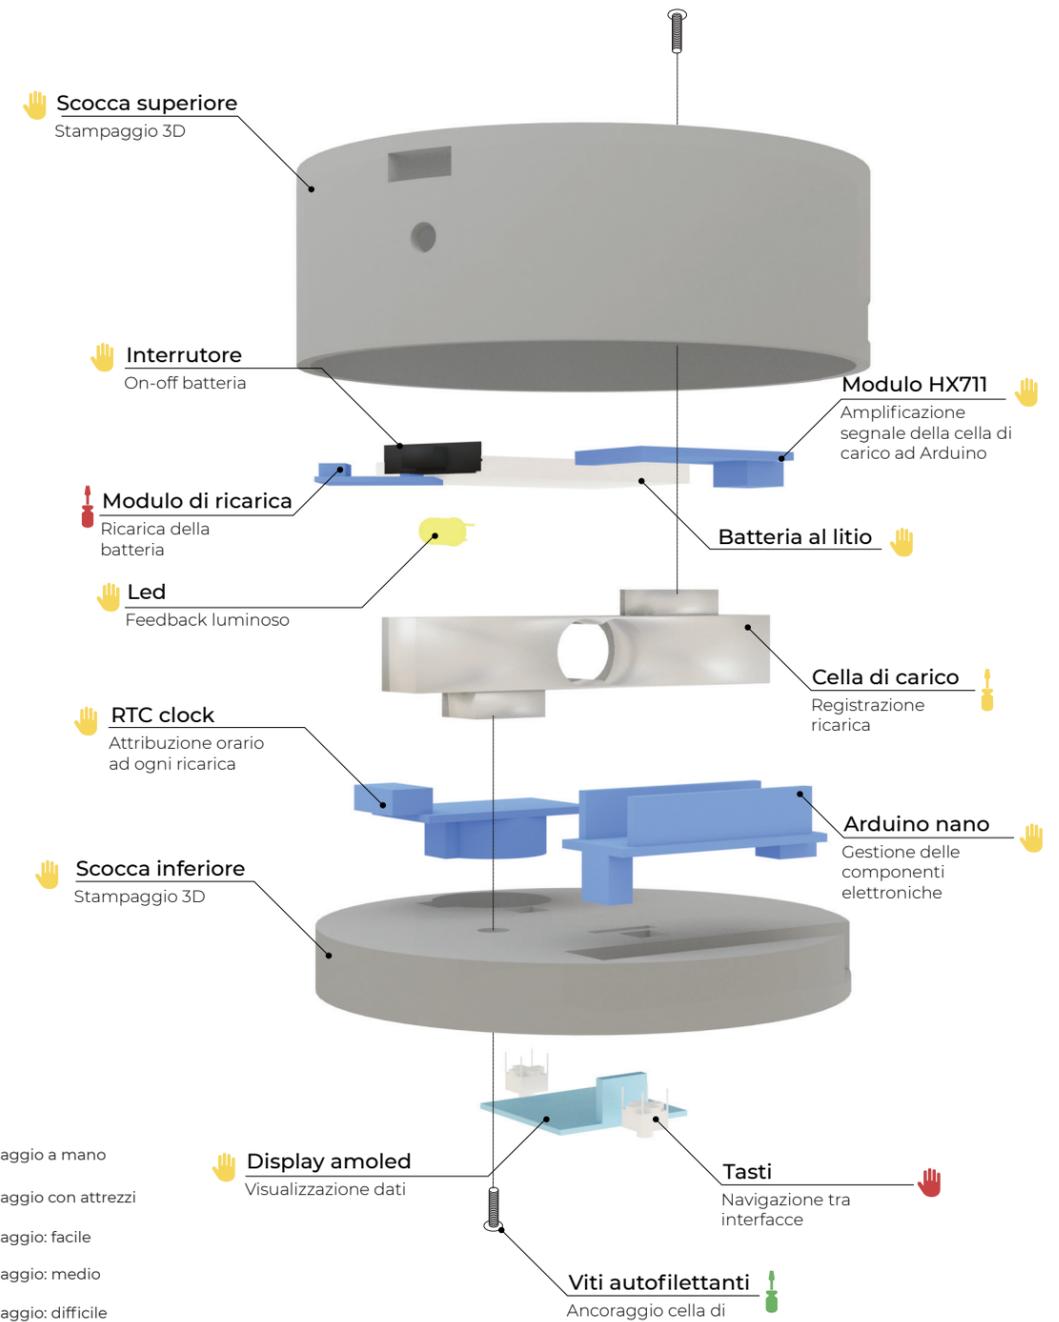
Schema di assemblaggio e disassemblaggio del prototipo.
